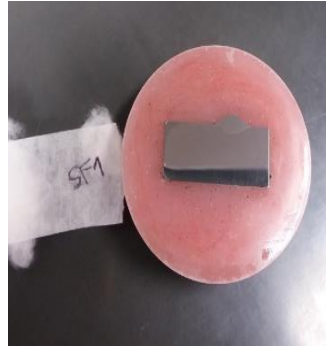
Sección transversal del cordón de soldadura fabricado con A-GMAW y aplicación de SiO₂
